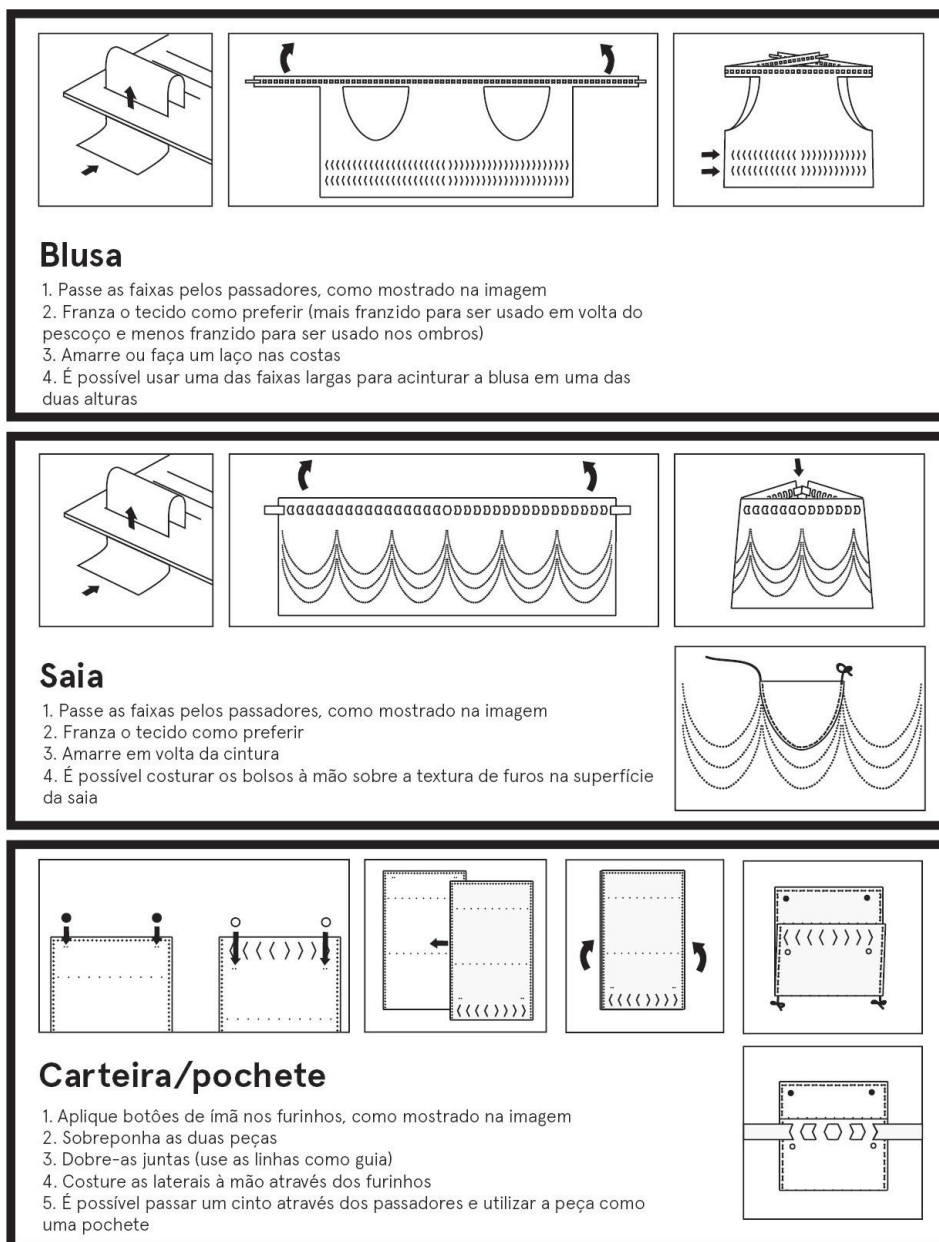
Instruções de montagem elaboradas pela Equipe 1
